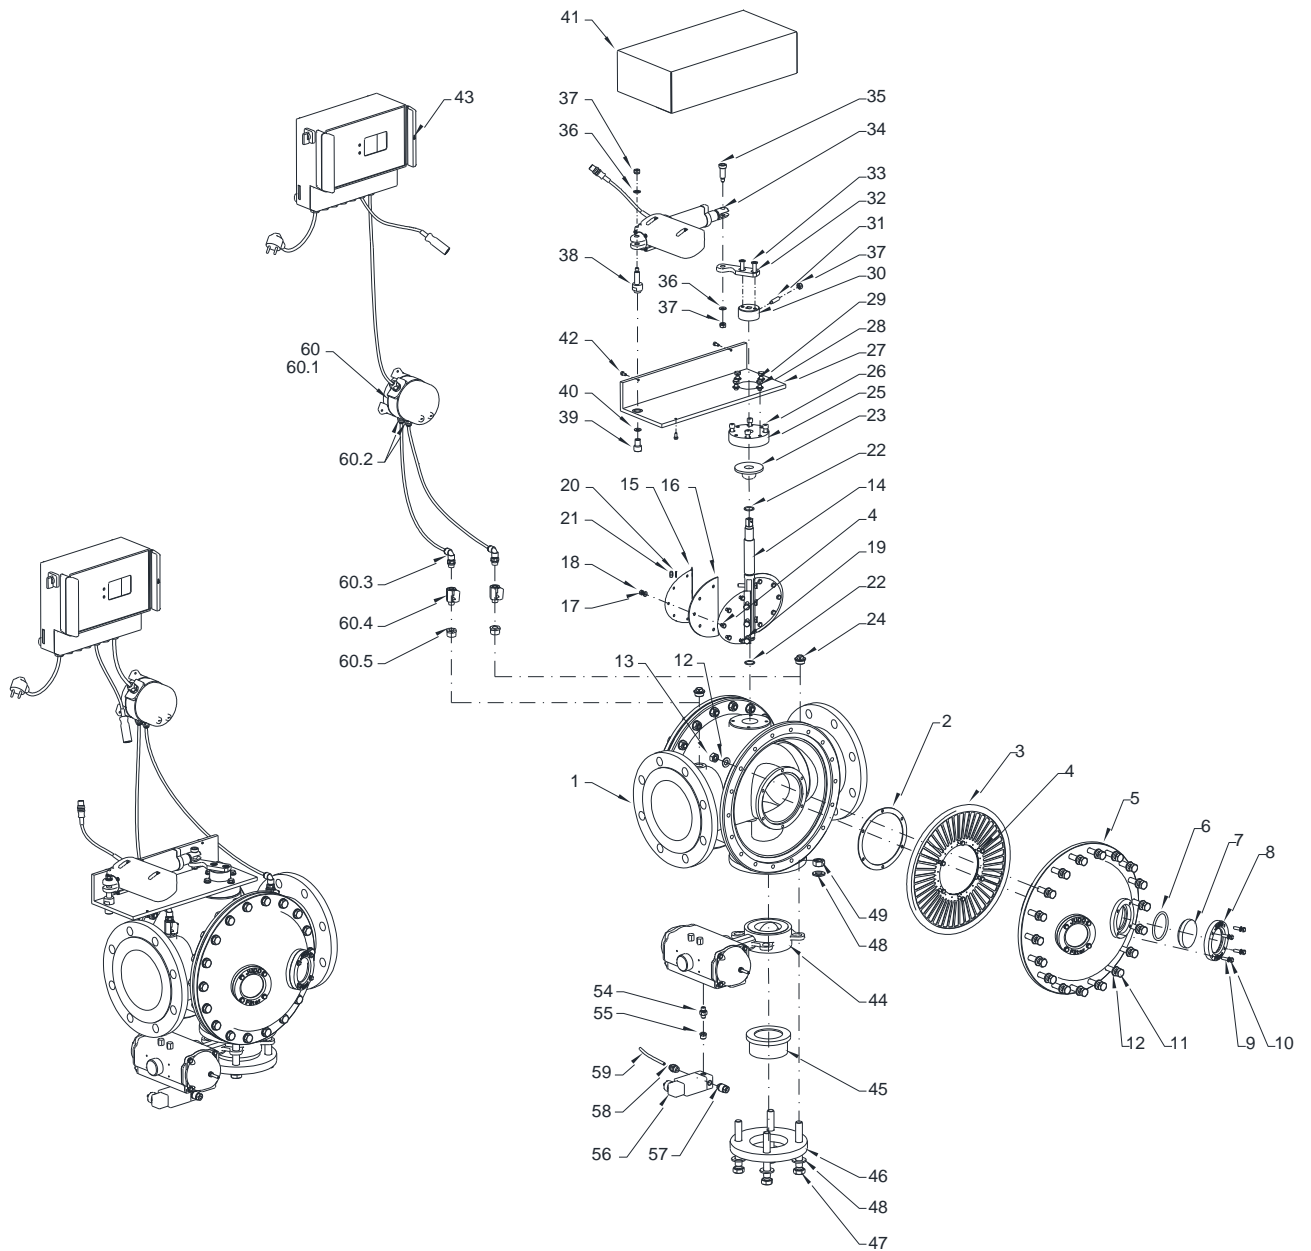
Explosionszeichnung JRSF-ATP DN150
